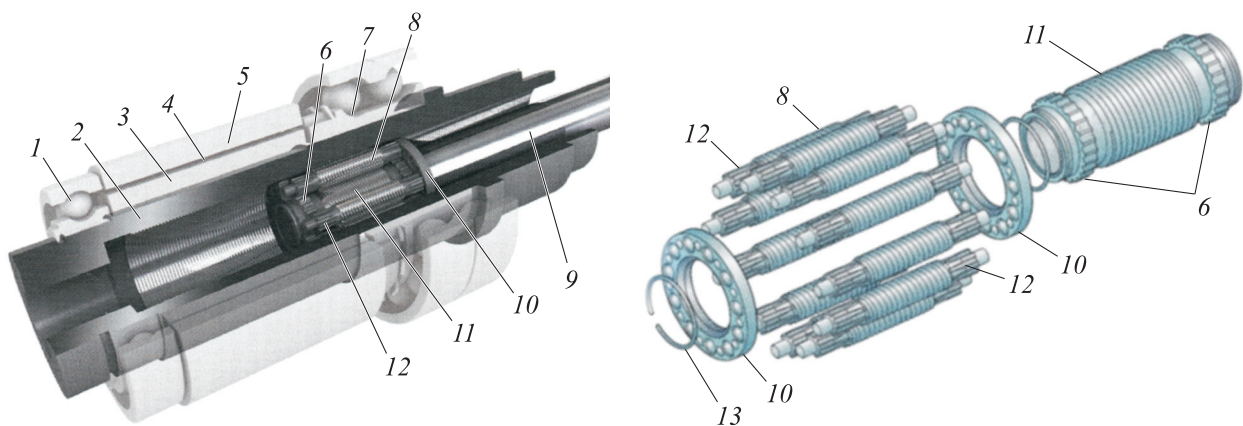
Внешний вид (а) и конструктивная схема (б) ПРВМ с ведущей гайкой:
